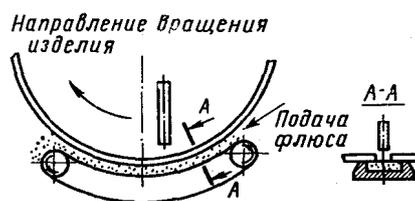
Схема флюсоремной подушки для сварки кольцевых швов
